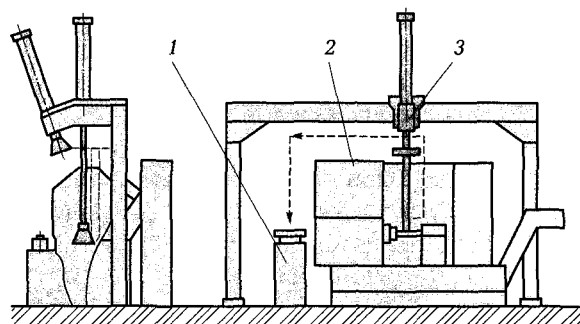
Роботизированный технологический комплекс на базе токарного станка с ЧПУ:
